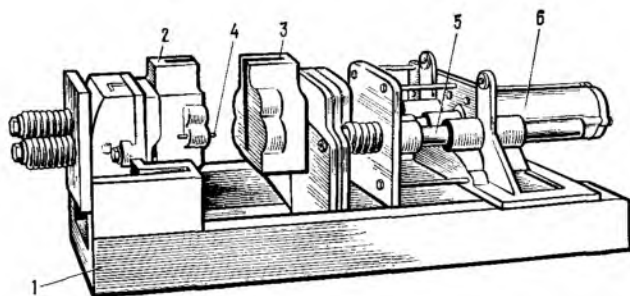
Пневматический кокильный станок конструкции МВТУ им. Баумана
